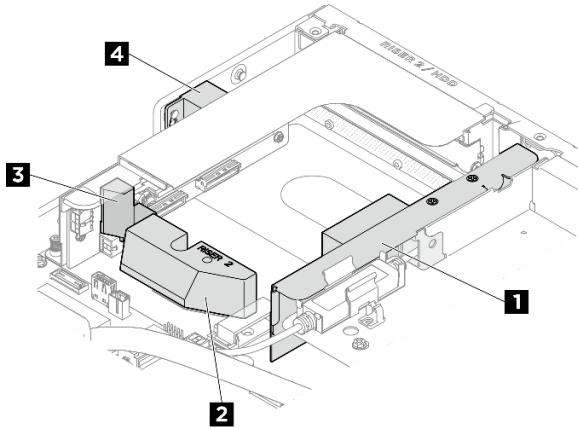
Position der DPU-Luftführung im Steckplatz für Adapterkarte 2
